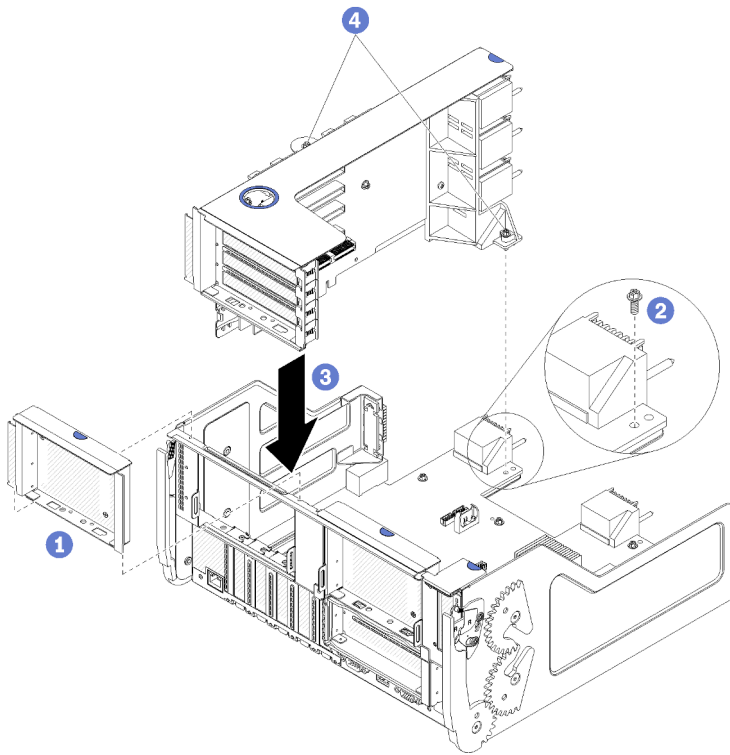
Instalación de la expansión para las ranuras 1 a 4 (expansión 1)
